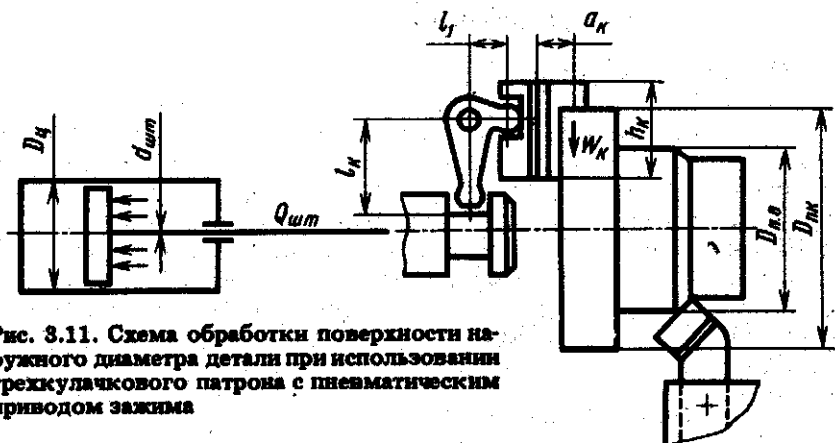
Схема обработки поверхности наружного диаметра детали при использовании трехкулачкового патрона с пневматическим приводом зажима
